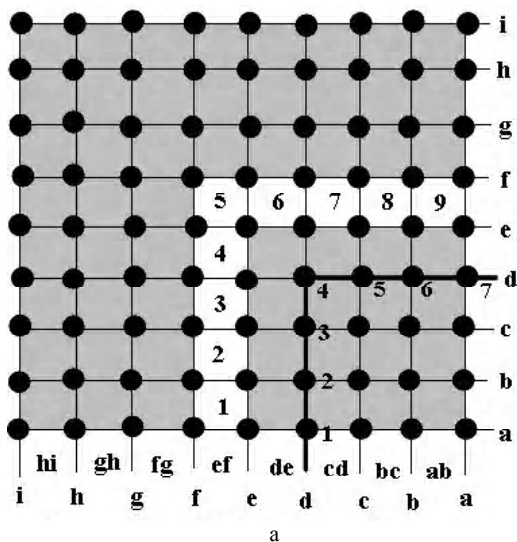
Верхняя левая часть корпуса BGA с 324 матрично-расположенными контактами
